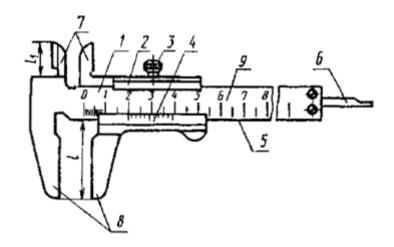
штангенциркуль двусторонний с глубиномером
